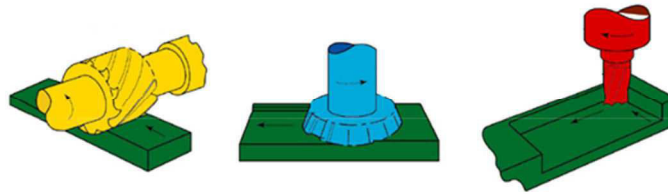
Métodos de fresagem [FONTE: adaptado [61]].
